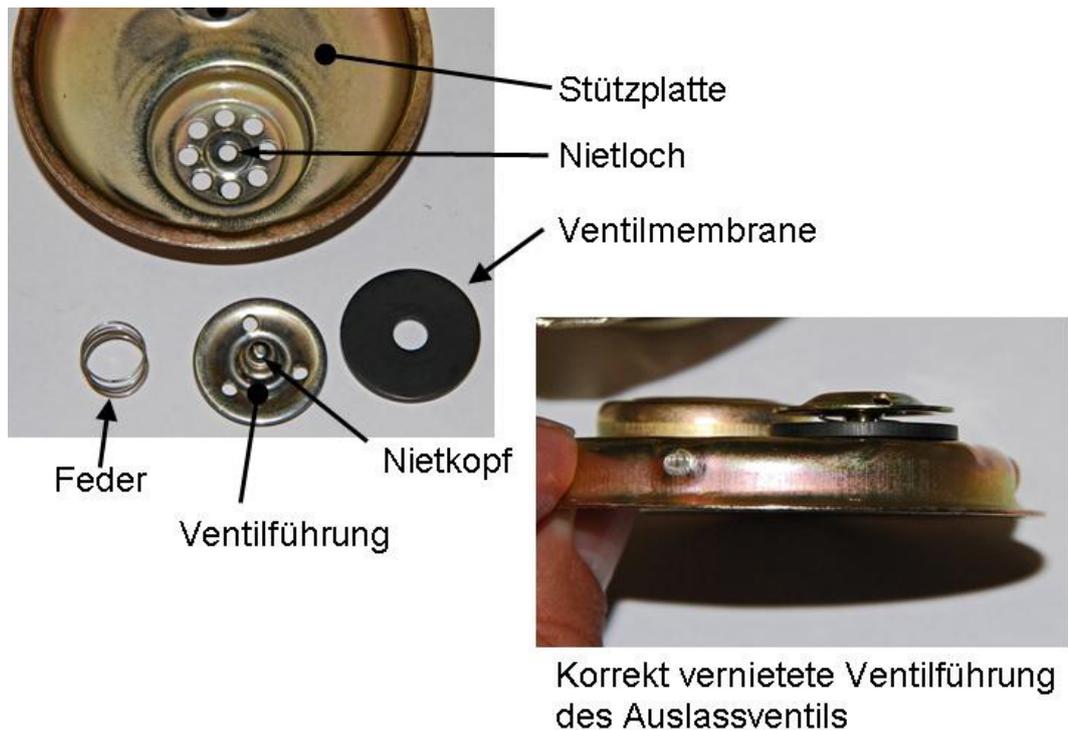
Einzelteile des defekten Rückschlagventils der mechanischen Treibstoffpumpe
